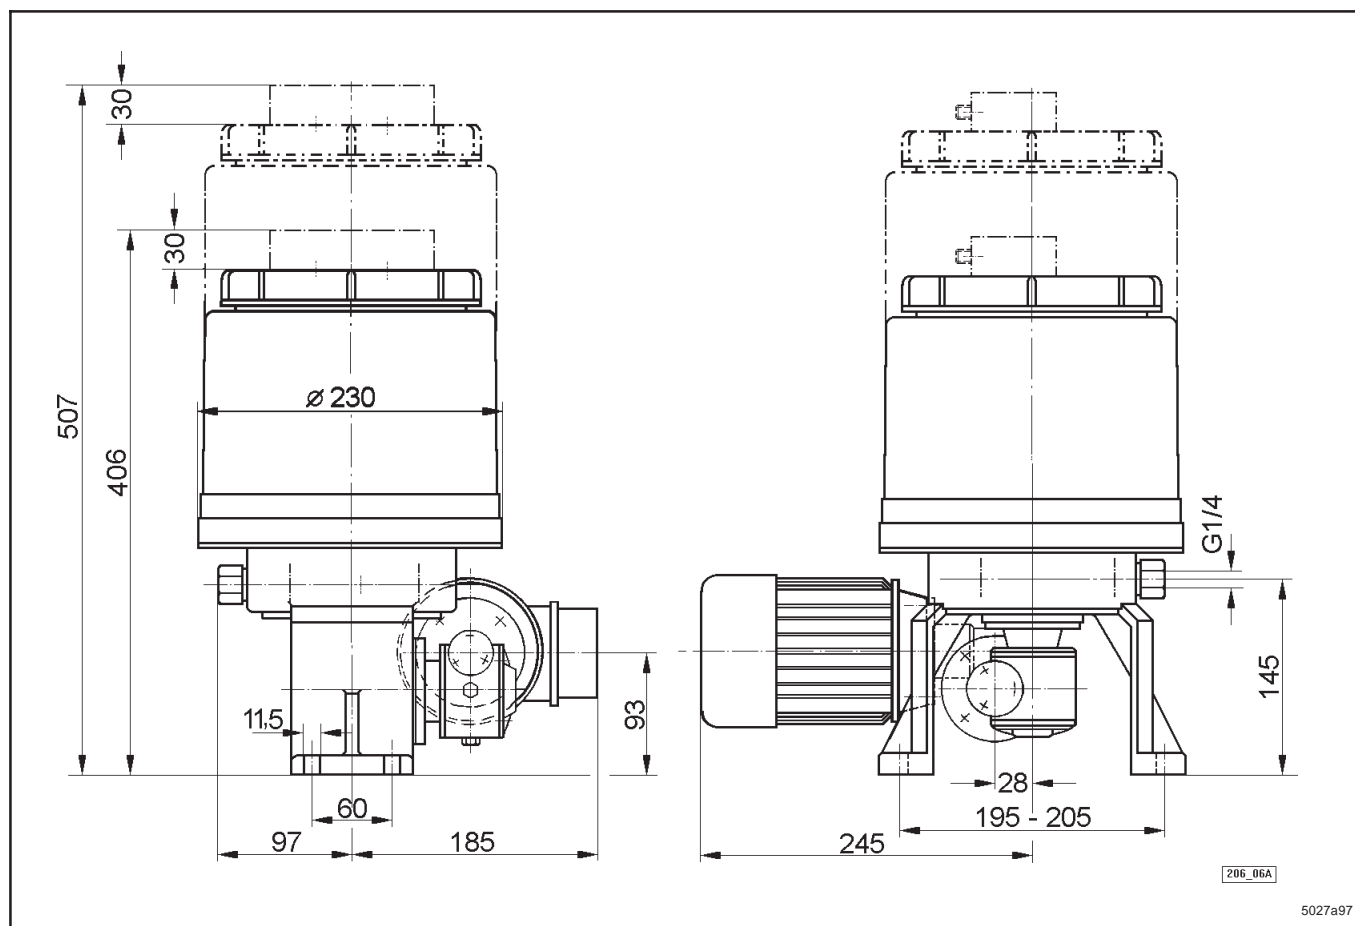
Maßzeichnung für Pumpe P205, 2-stufiges Getriebe, 4/8l Kunststoffbehälter, Motorantrieb
